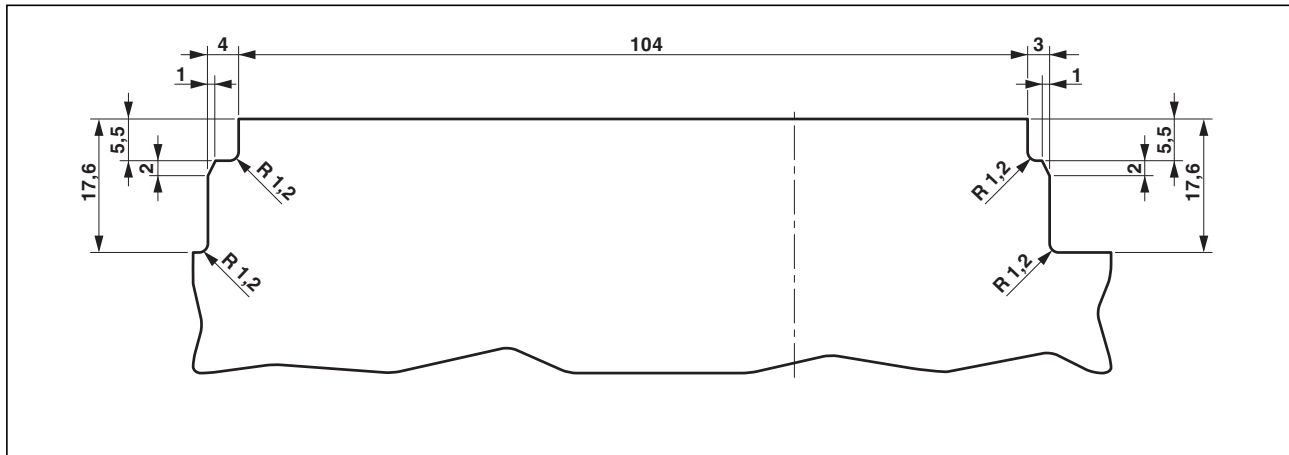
Maßzeichnung der Leiterplatte des Gehäuses bei Verwendung des Universaldeckels CL
